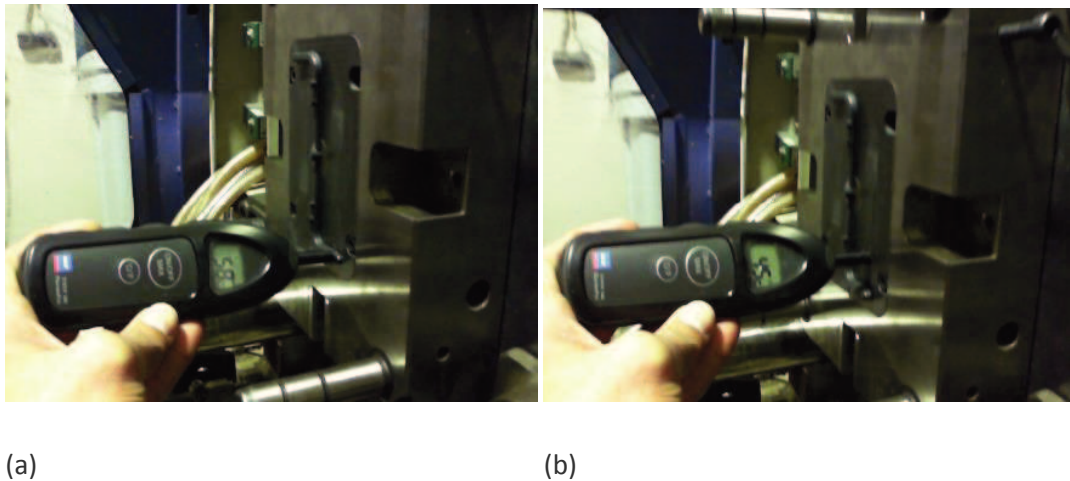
(a) Temperatura da peça moldada; (b) Temperatura da superfície moldante
